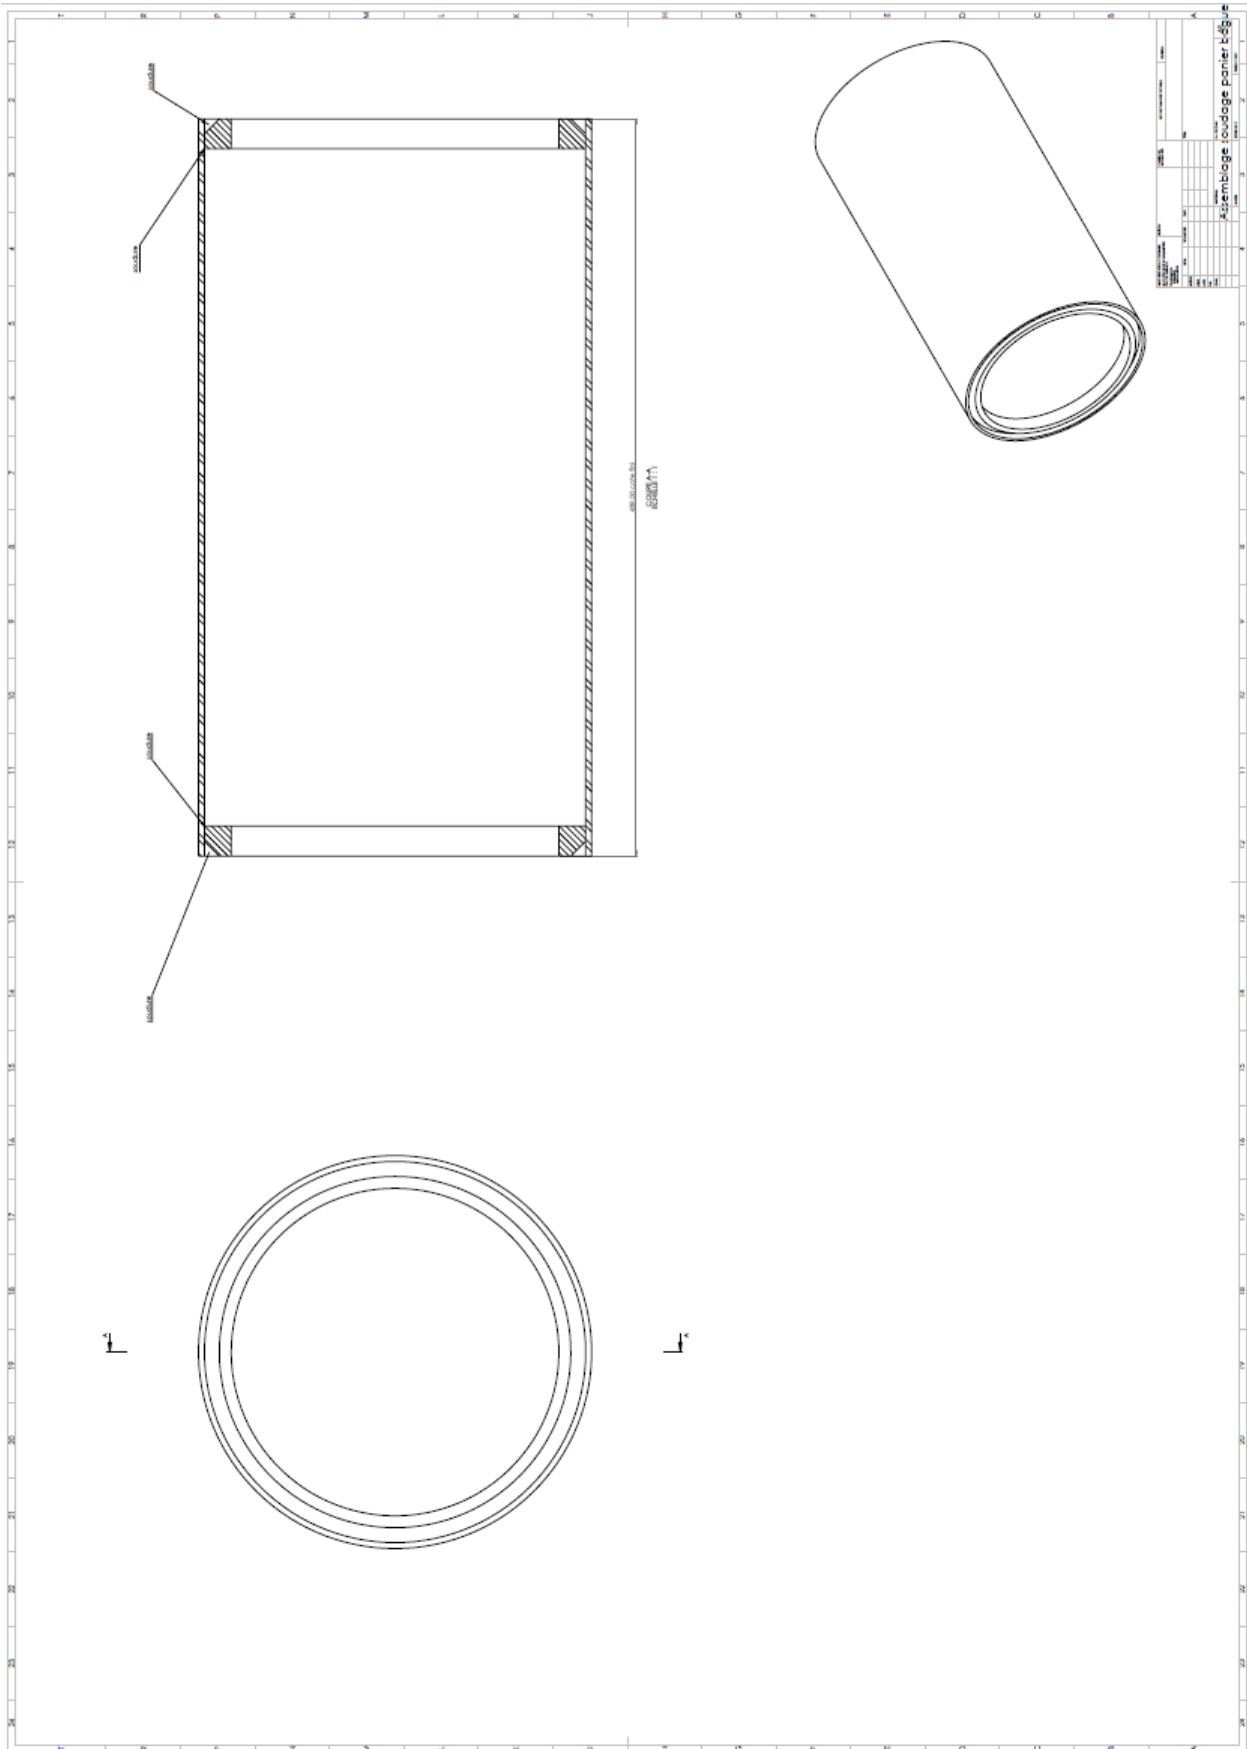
Plans de soudage du panier interne de la maquette.
